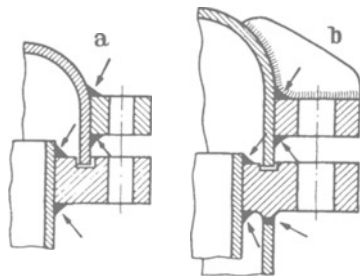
Deckelschweißungen bei Dampfgefäßverschlüssen.
